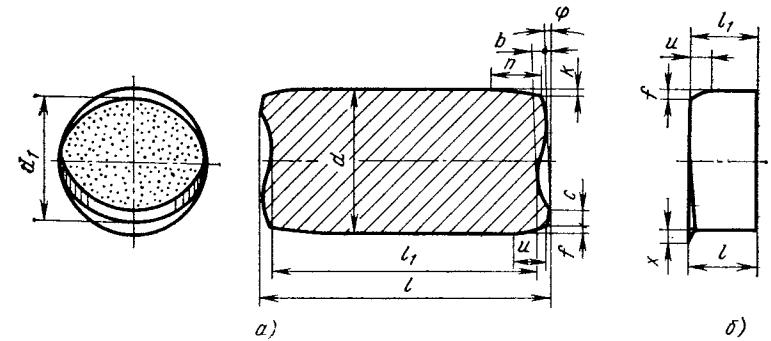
Схемы измерения заготовки, отрезанной не полностью открытой или не полностью закрытой резкой (а), и точной короткой заготовки (б), полученной закрытой резкой
